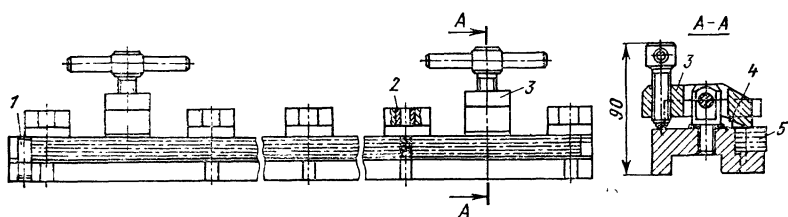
Переналаживаемый кондуктор для сверления отверстий в пакете тонких планок
